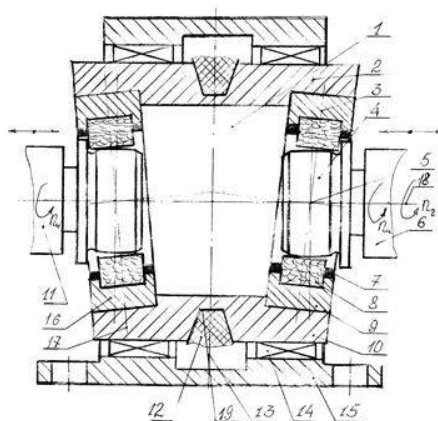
Устройство для безабразивной обработки дорожек качения подшипников
